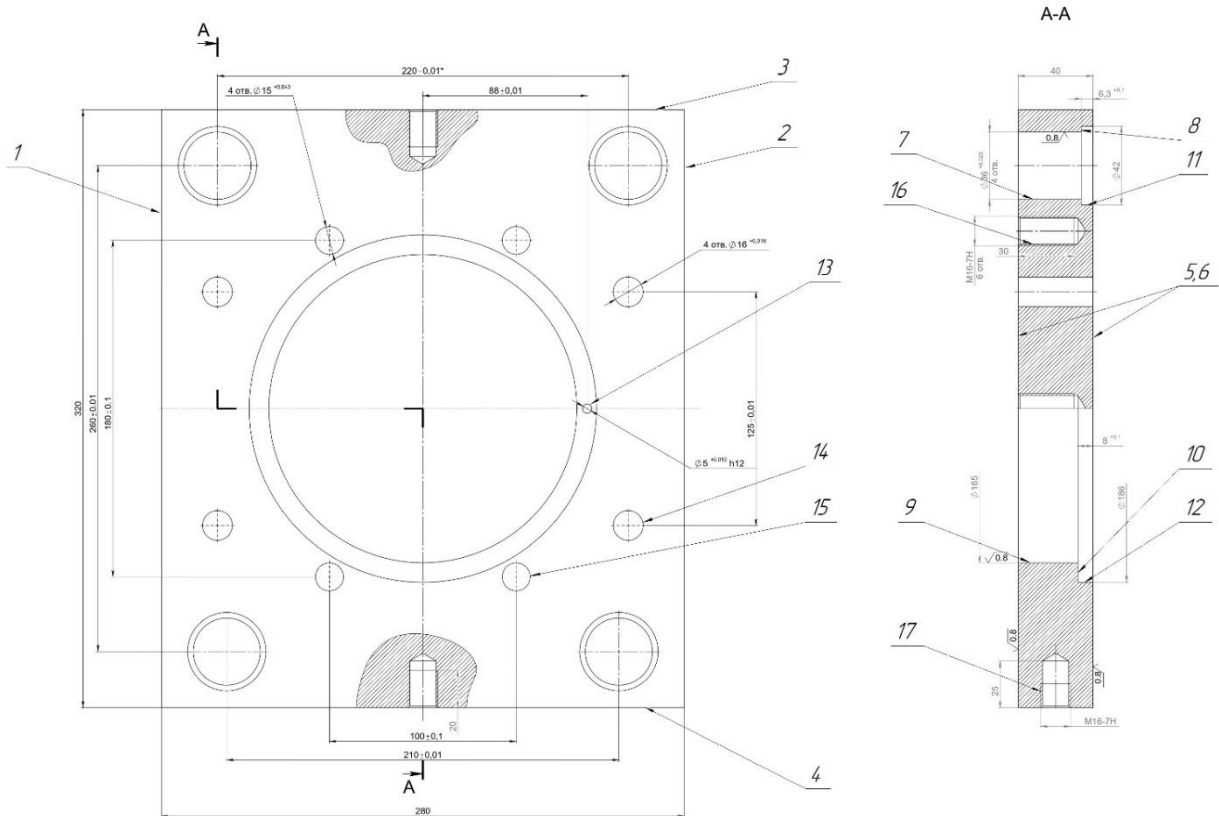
Ескіз деталі із номерами її поверхонь
